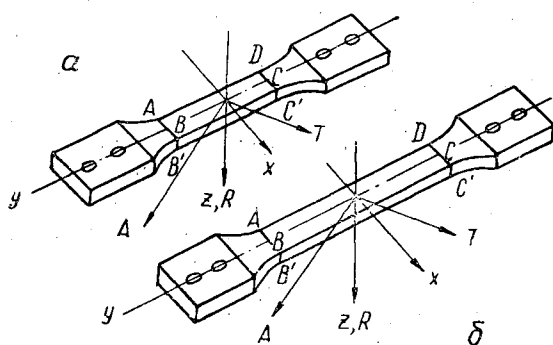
Образцы для испытаний на усталость: а — образец для машины ЛТА; б — для машины ЛКИ-1.
